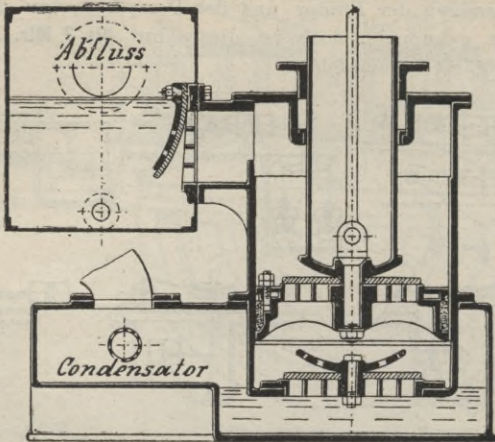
, für Schiffsmaschinen gebräuchlich, s. auch Seite 400.
